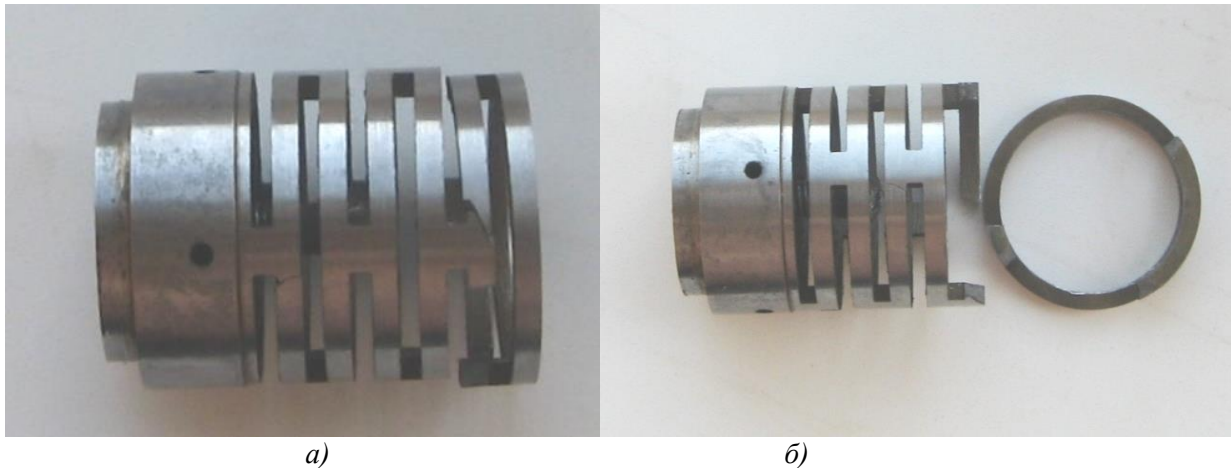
Дослідний зразок ППП, виготовлений з розрахунком за формулою (5) боковим зазором S між робочими кільцями пружинної частини ППП і поверхнею розточки корпусу пристрою
